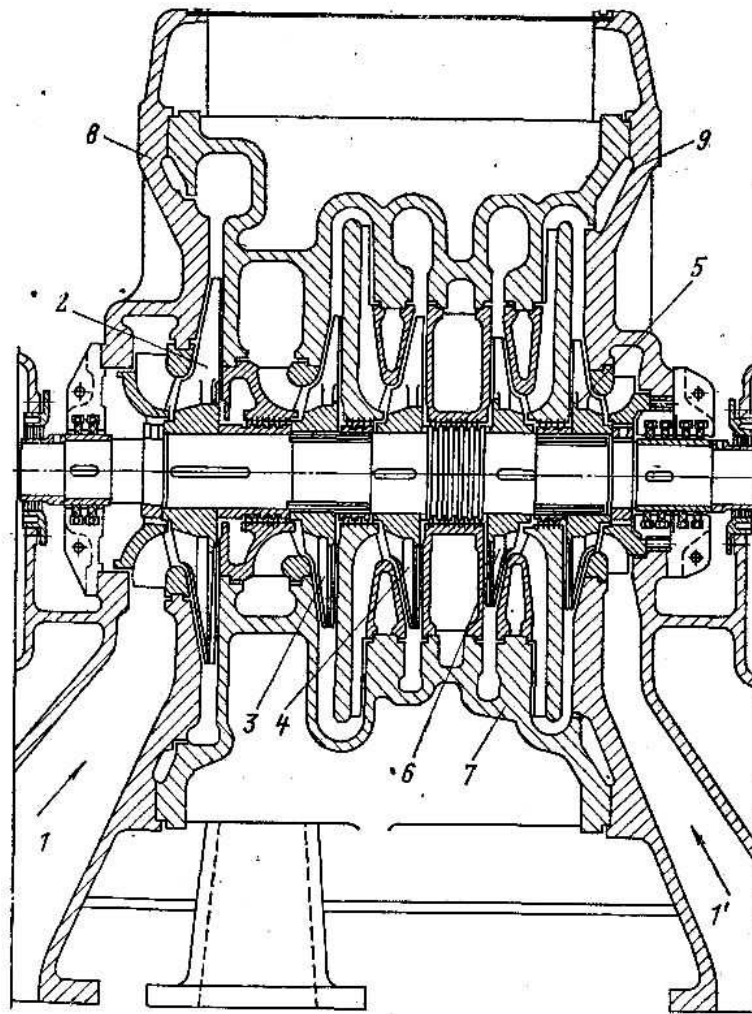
Поздовжній переріз другого корпуса турбокомпресора
